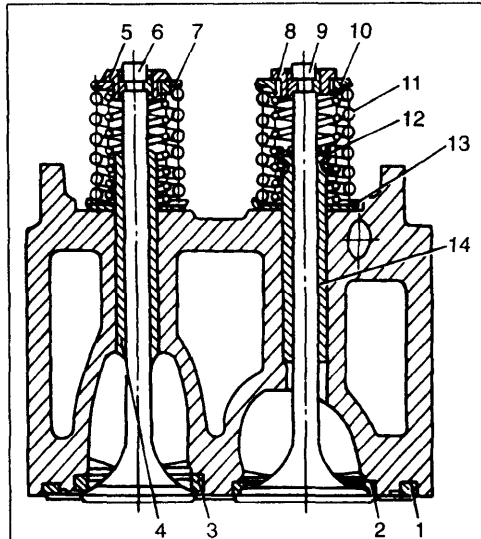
Головка цилиндров с впускным и выпускным клапанами:
